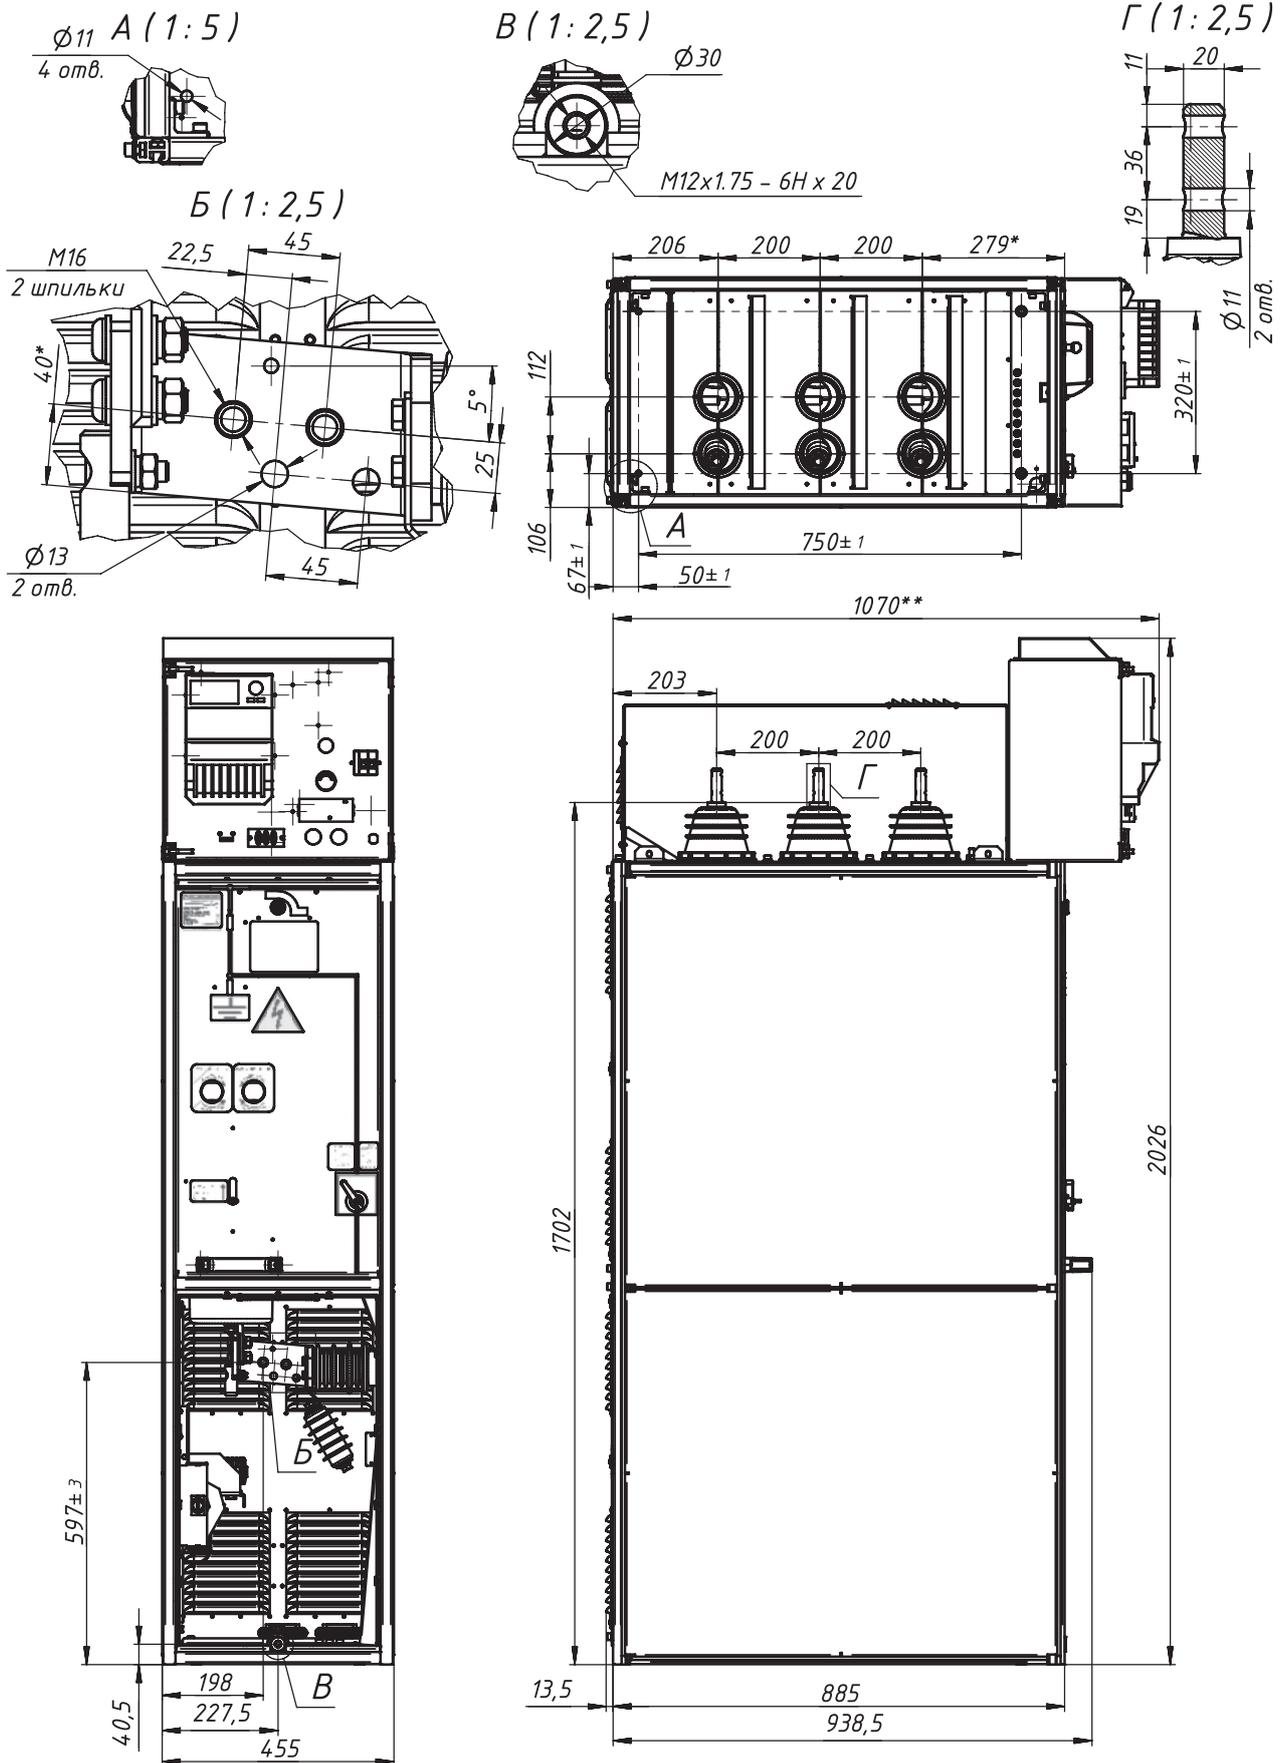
КРУ/Вертикаль-10-20/1000. Габаритный чертёж
